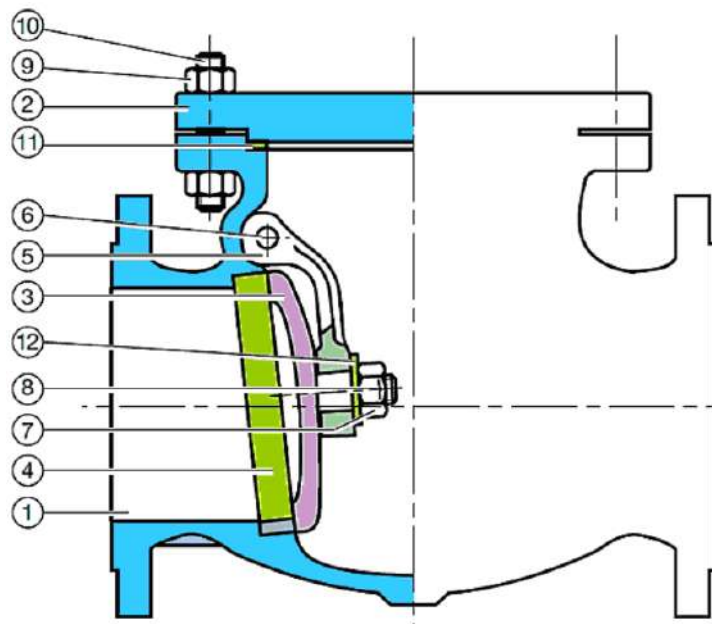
Конструктивні елементи зворотного клапана.
